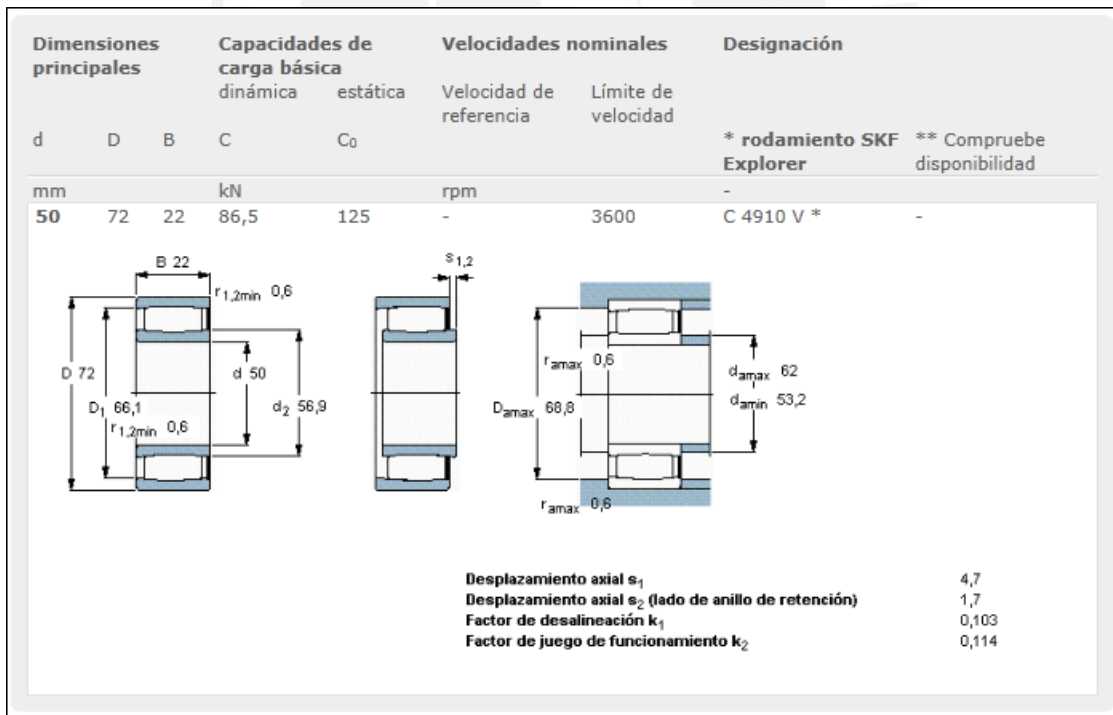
Ficha técnica del rodamiento C4910V
